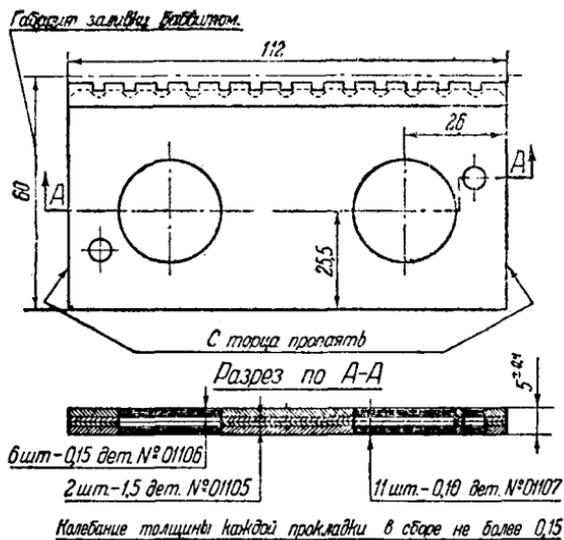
Дет. № 01104. Прокладка среднего подшипника в сборе
